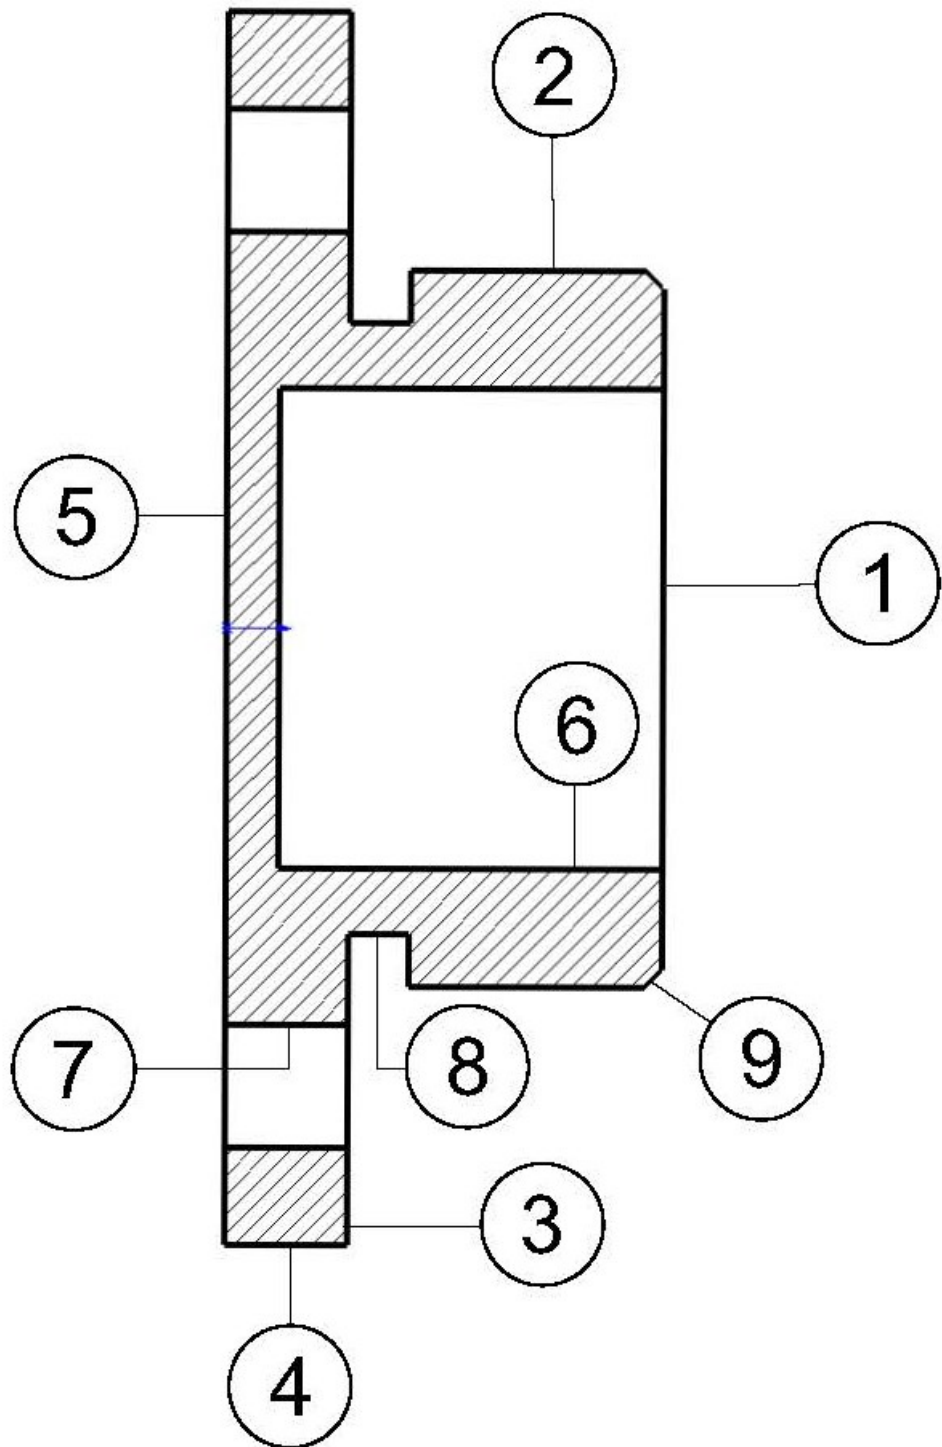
Ескіз оброблених поверхонь деталі
